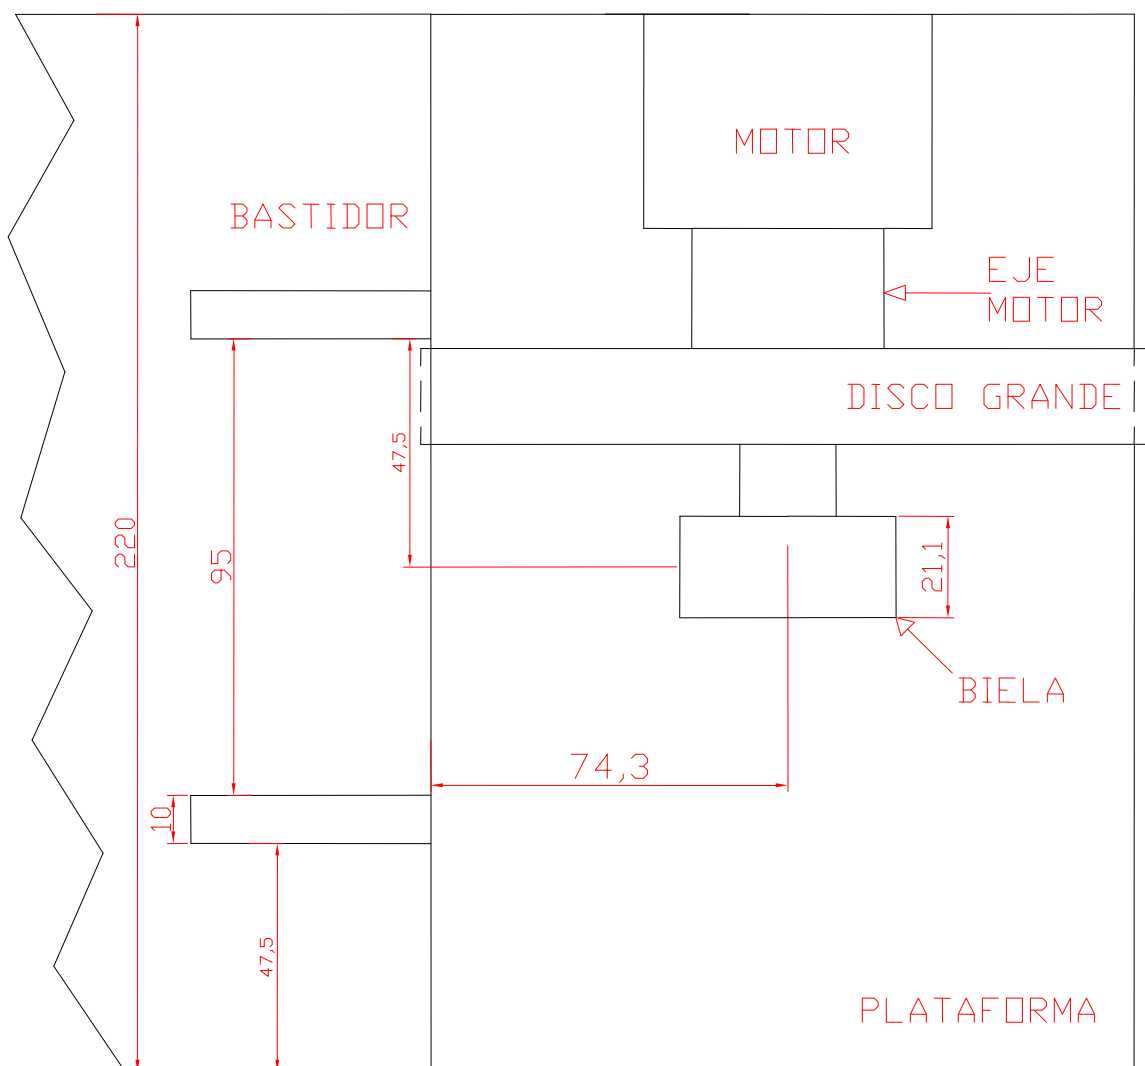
Vista en Planta Esquemática de la Máquina.
